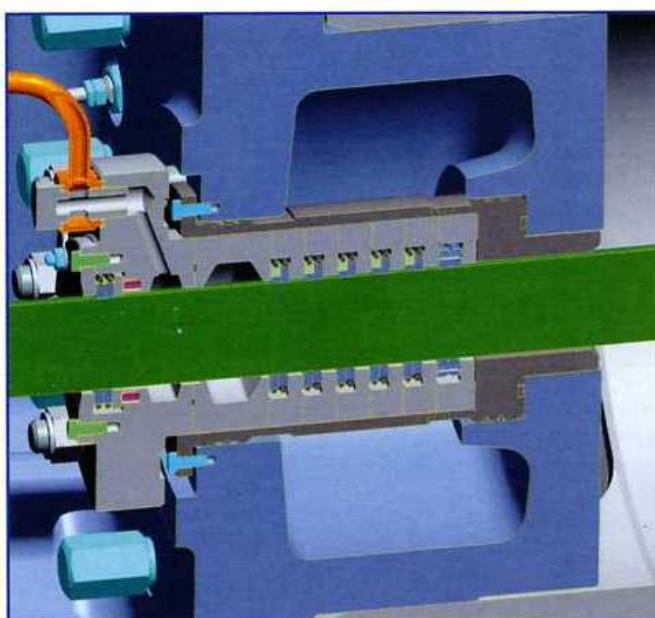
Общий вид промежуточного фонаря и уплотнения штока
